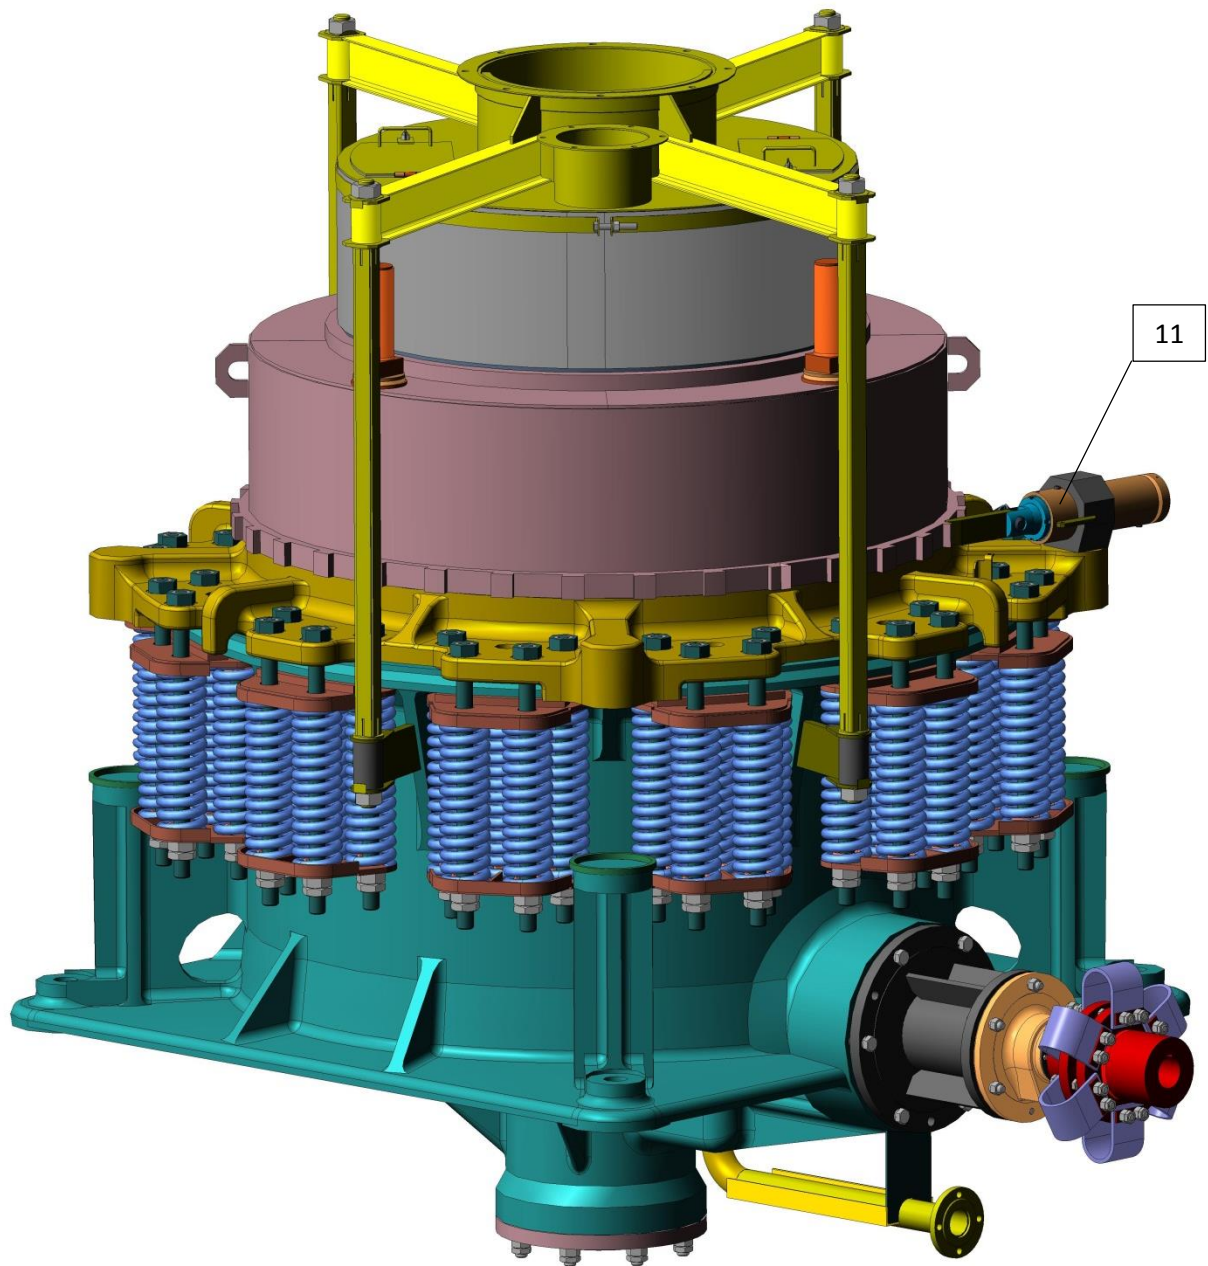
Механизм дробилки 1200. Общий вид.
